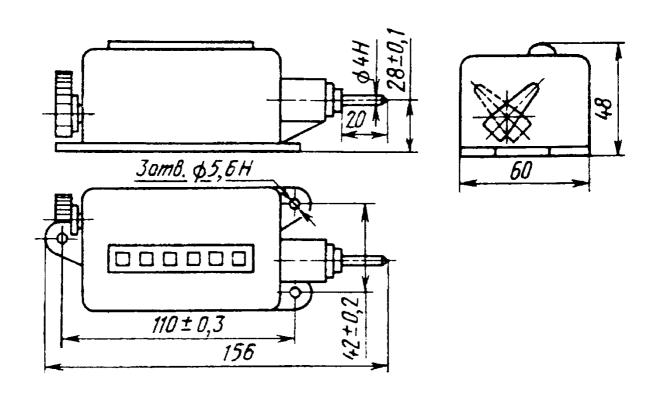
Основные габаритные и присоединительные размеры счетчика оборотов
